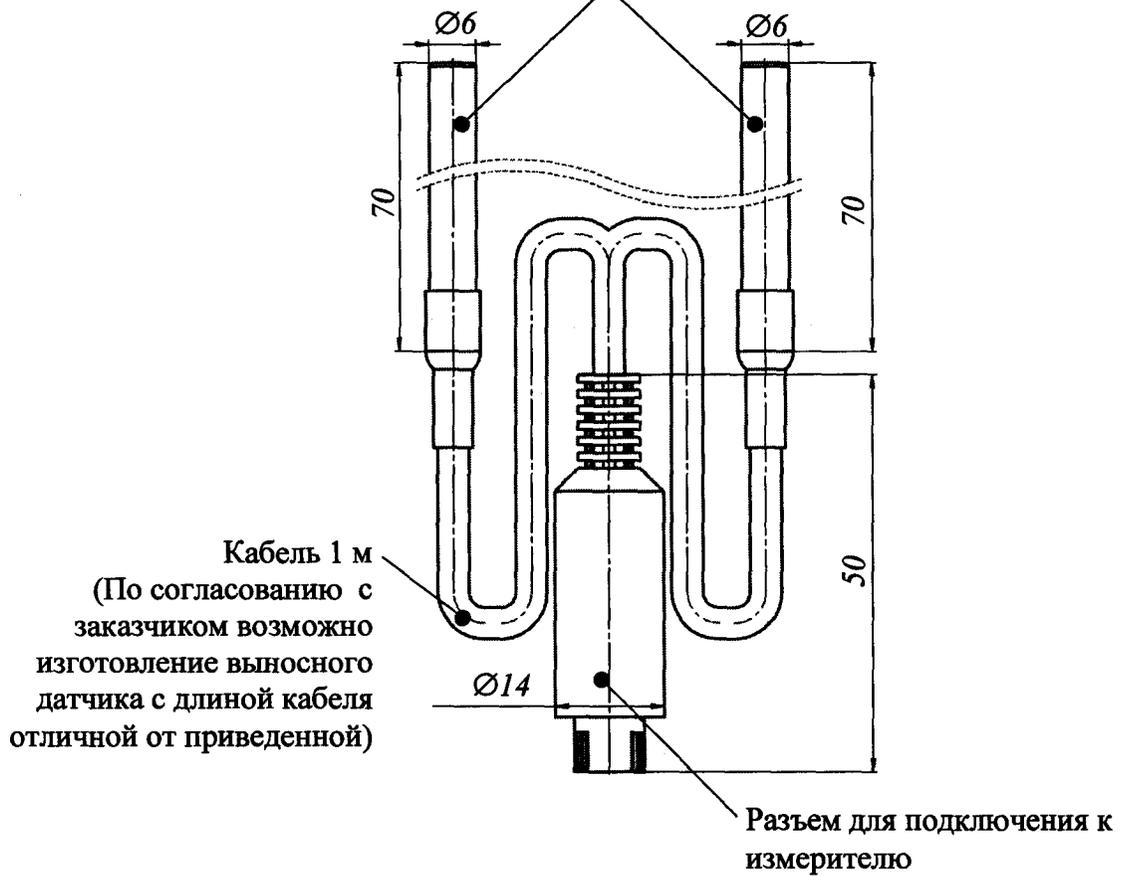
Внешний вид и габаритные размеры датчика температуры для прибора измерительного модификации ПИ-002/10.
